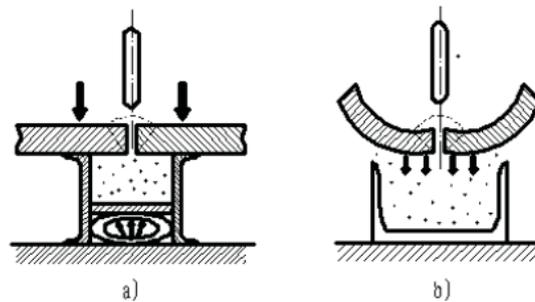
Diagrama esquemático de la soldadura de respaldo de fundente
